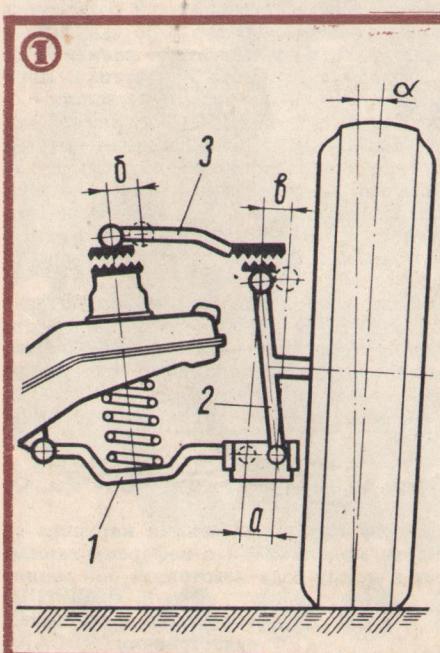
Схема передней подвески: 1 — нижний рычаг; 2 — поворотная стойка; 3 — верхний рычаг.
